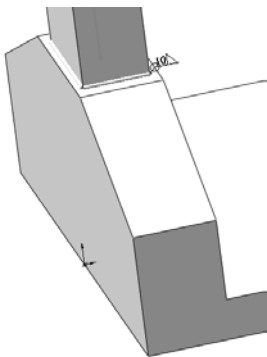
创建半径为 10.00mm 的焊缝
